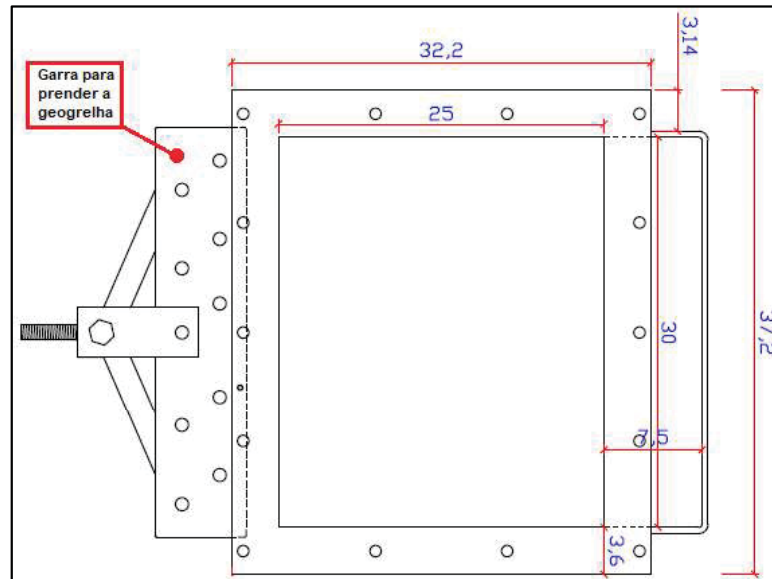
Vista superior da caixa e detalhe das porcas soldadas na parte inferior da borda
